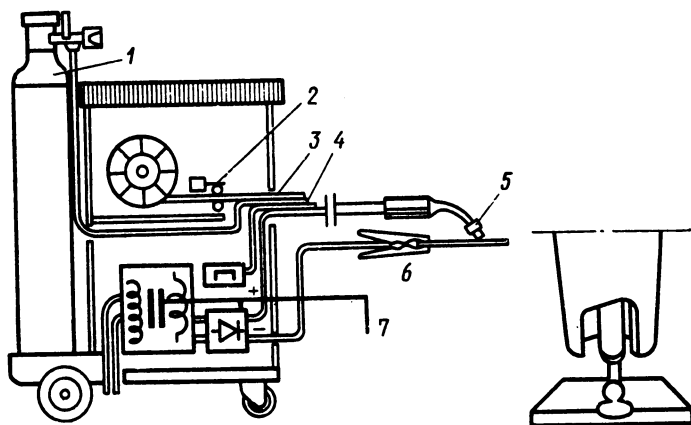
Полуавтомат для сварки в среде защитных газов:
